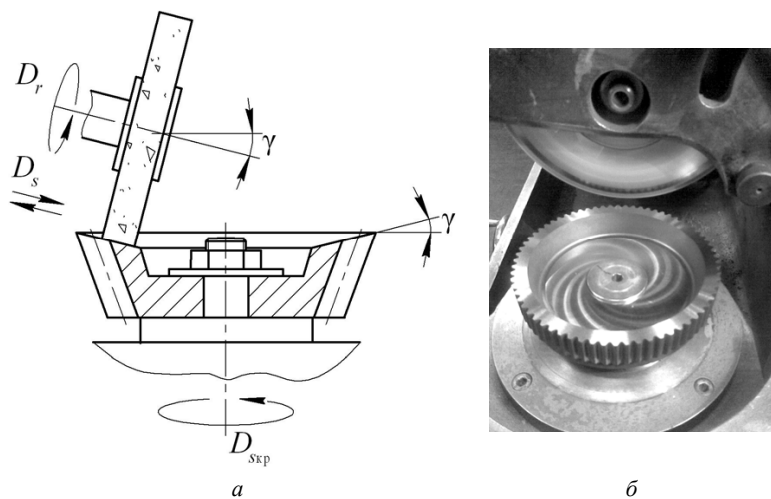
Заточка долбяка по передней поверхности: а) схема настройки; б) процесс заточки
